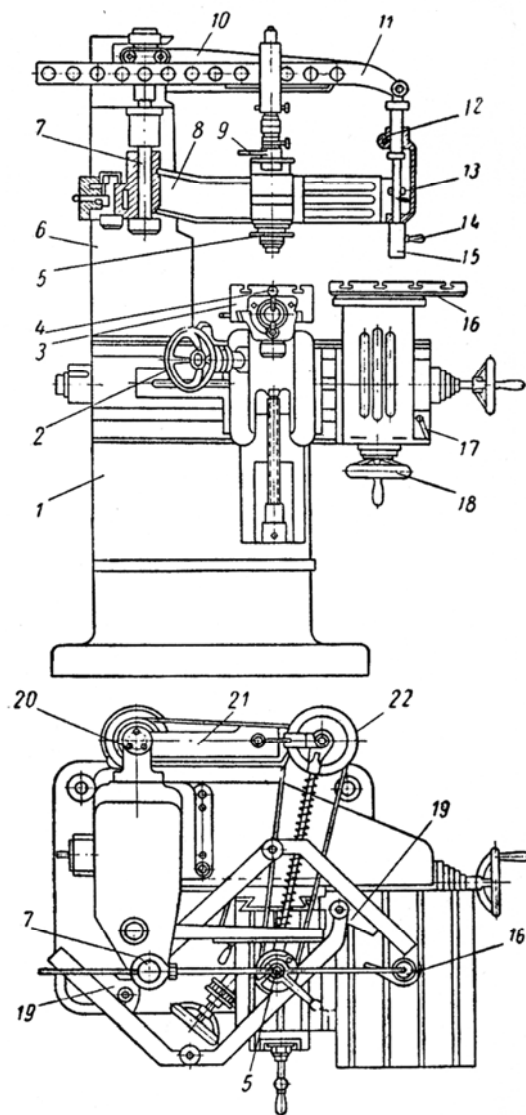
Копировально-фрезерный станок мод. 6461:
